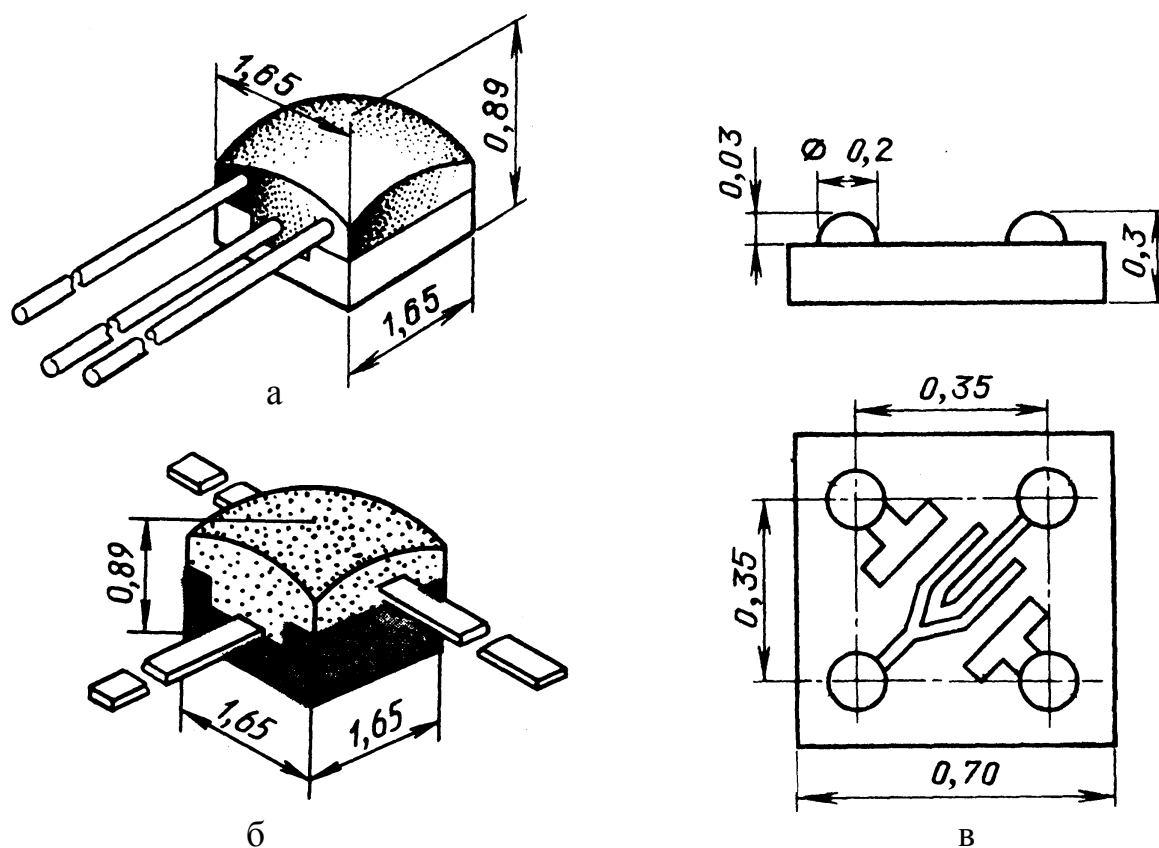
Конструкции бескорпусного биполярного транзистора с гибкими (а), балочными (б) и шариковыми (в) выводами.
